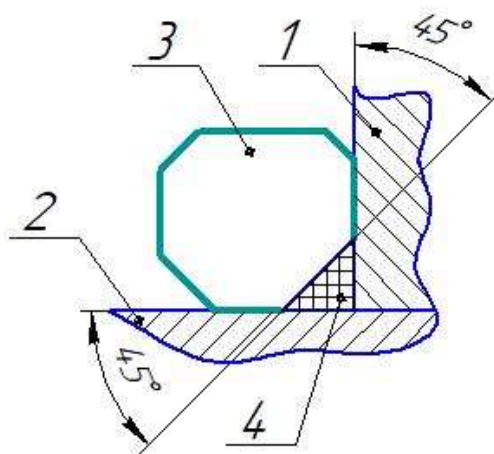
Общий вид определения катета углового сварного шва
